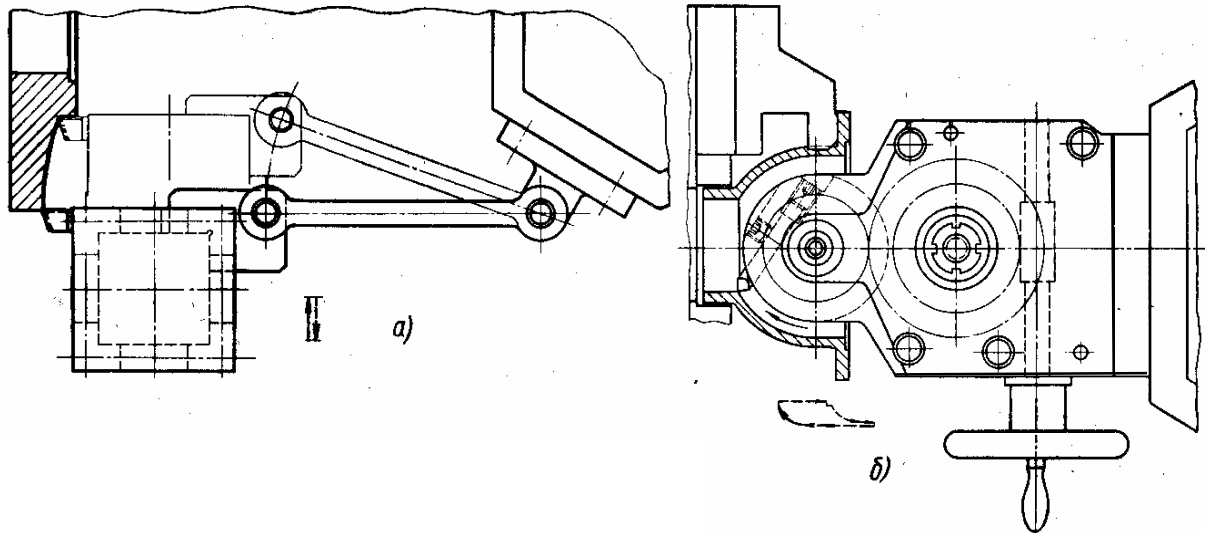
Пристосування для обробки сферичних поверхонь: а - важільне; б - черв'ячне
